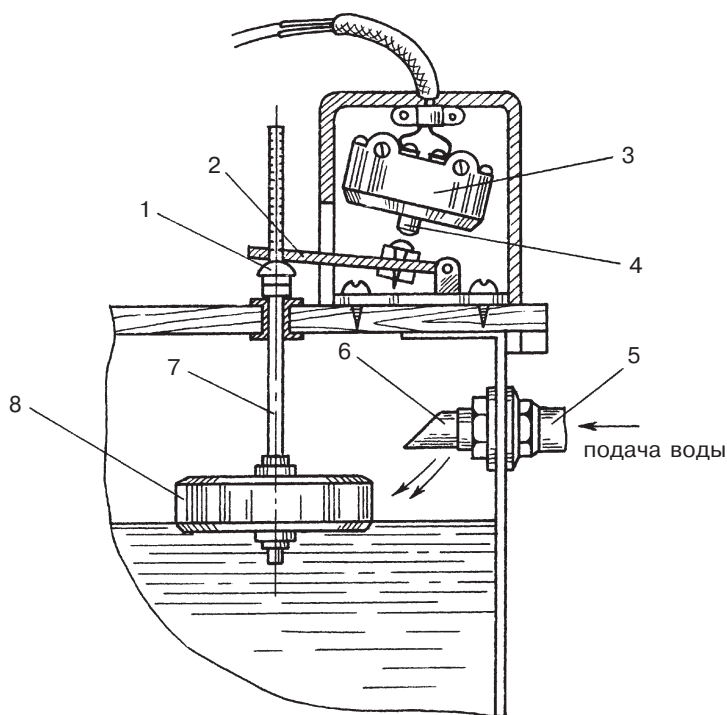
Поплавковый регулятор уровня: 1 — упор-гайка; 2 — рычаг; 3 — микропереключатель; 4 — толкатель; 5 — патрубок; 6 — отражатель; 7 — шток; 8 — поплавок
